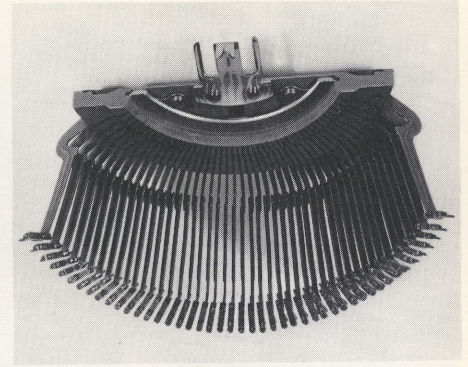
Komplettes Segment mit montierten Typenhebeln und Zentralführung
